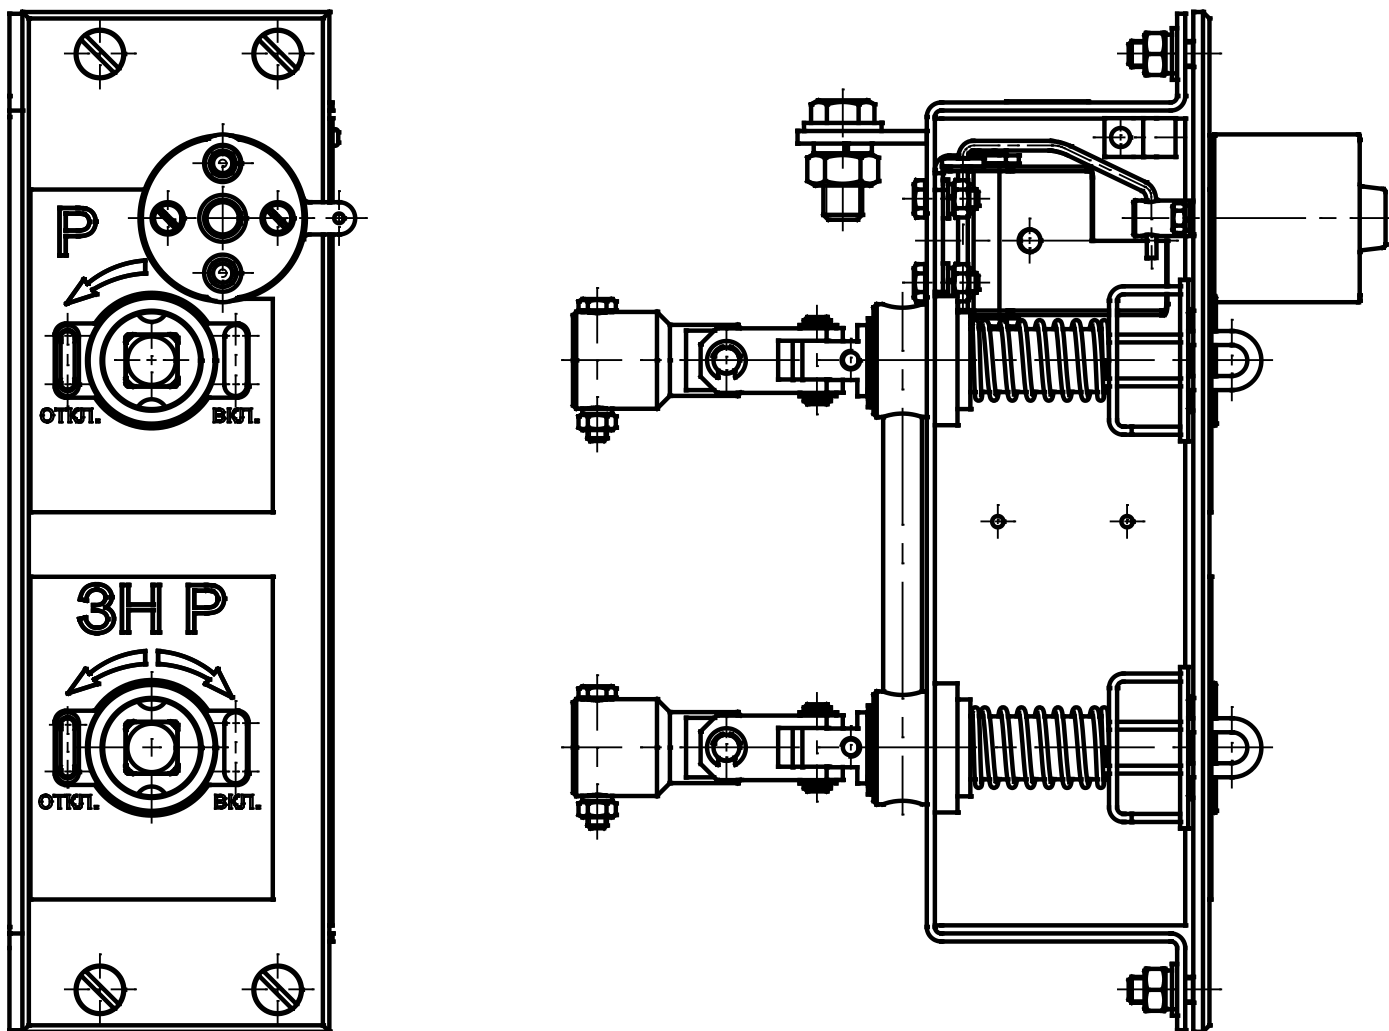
Привод ПРК-10Б-23 для разъединителя РВЗ-К-1Н-10/630(1000) с магнитным блок-замком на главных ножах.
